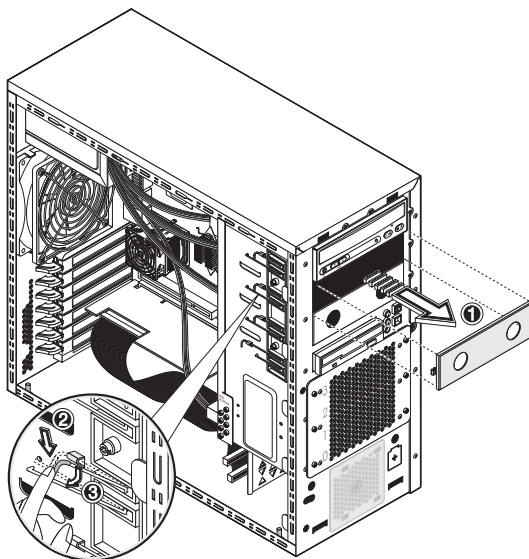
Подготовка универсального гнезда для установки дисковод
